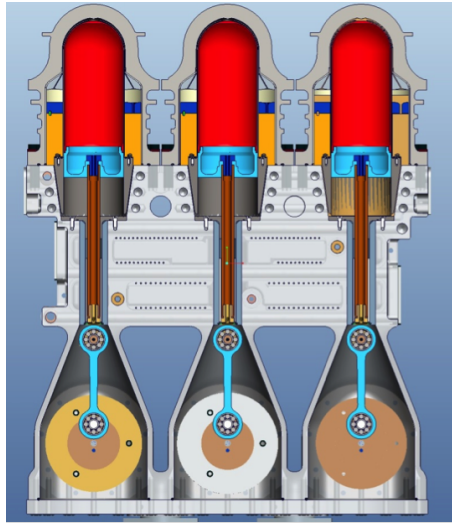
Vue CAO du compresseur thermique BoostHeat.
